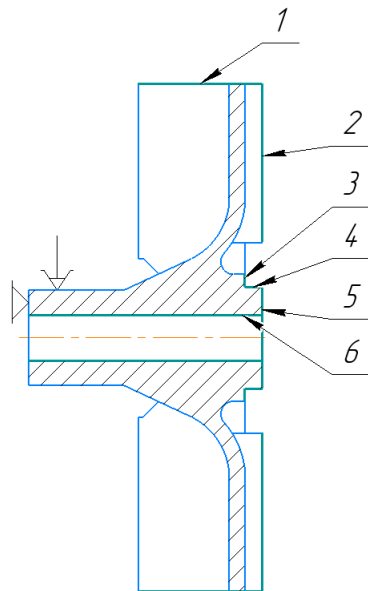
Ескіз токарної чорнкової операції 025
